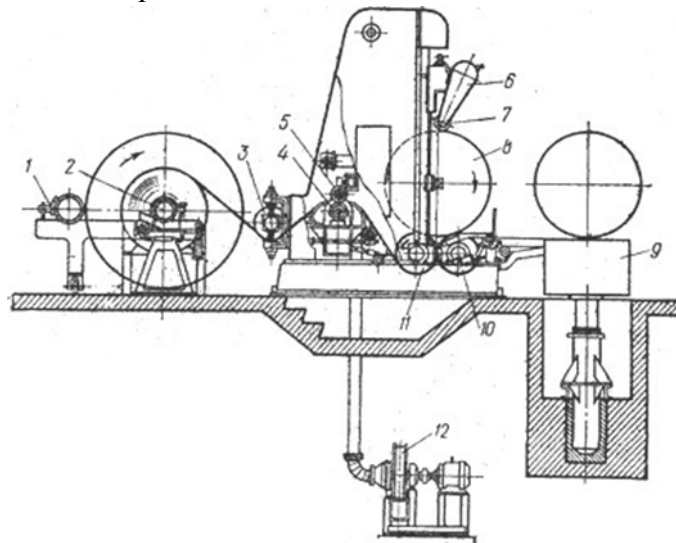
Поздовжньо-різальний станок з нижньою заправкою паперу: 1 – гальмівний пристрій для зупинки тамбурного валу, 2 – розкат, 3 – папероведучий валик, 4 – чашечні ножі, 5 – дискові ножі, 6 – привід притискного валу, 7 – притискний вал, 8 – намотувальний рулон, 9 – стіл для опускання рулону, 10 і 11 – несучі вали, 12 – вентилятор-розривач для видалення кромки
